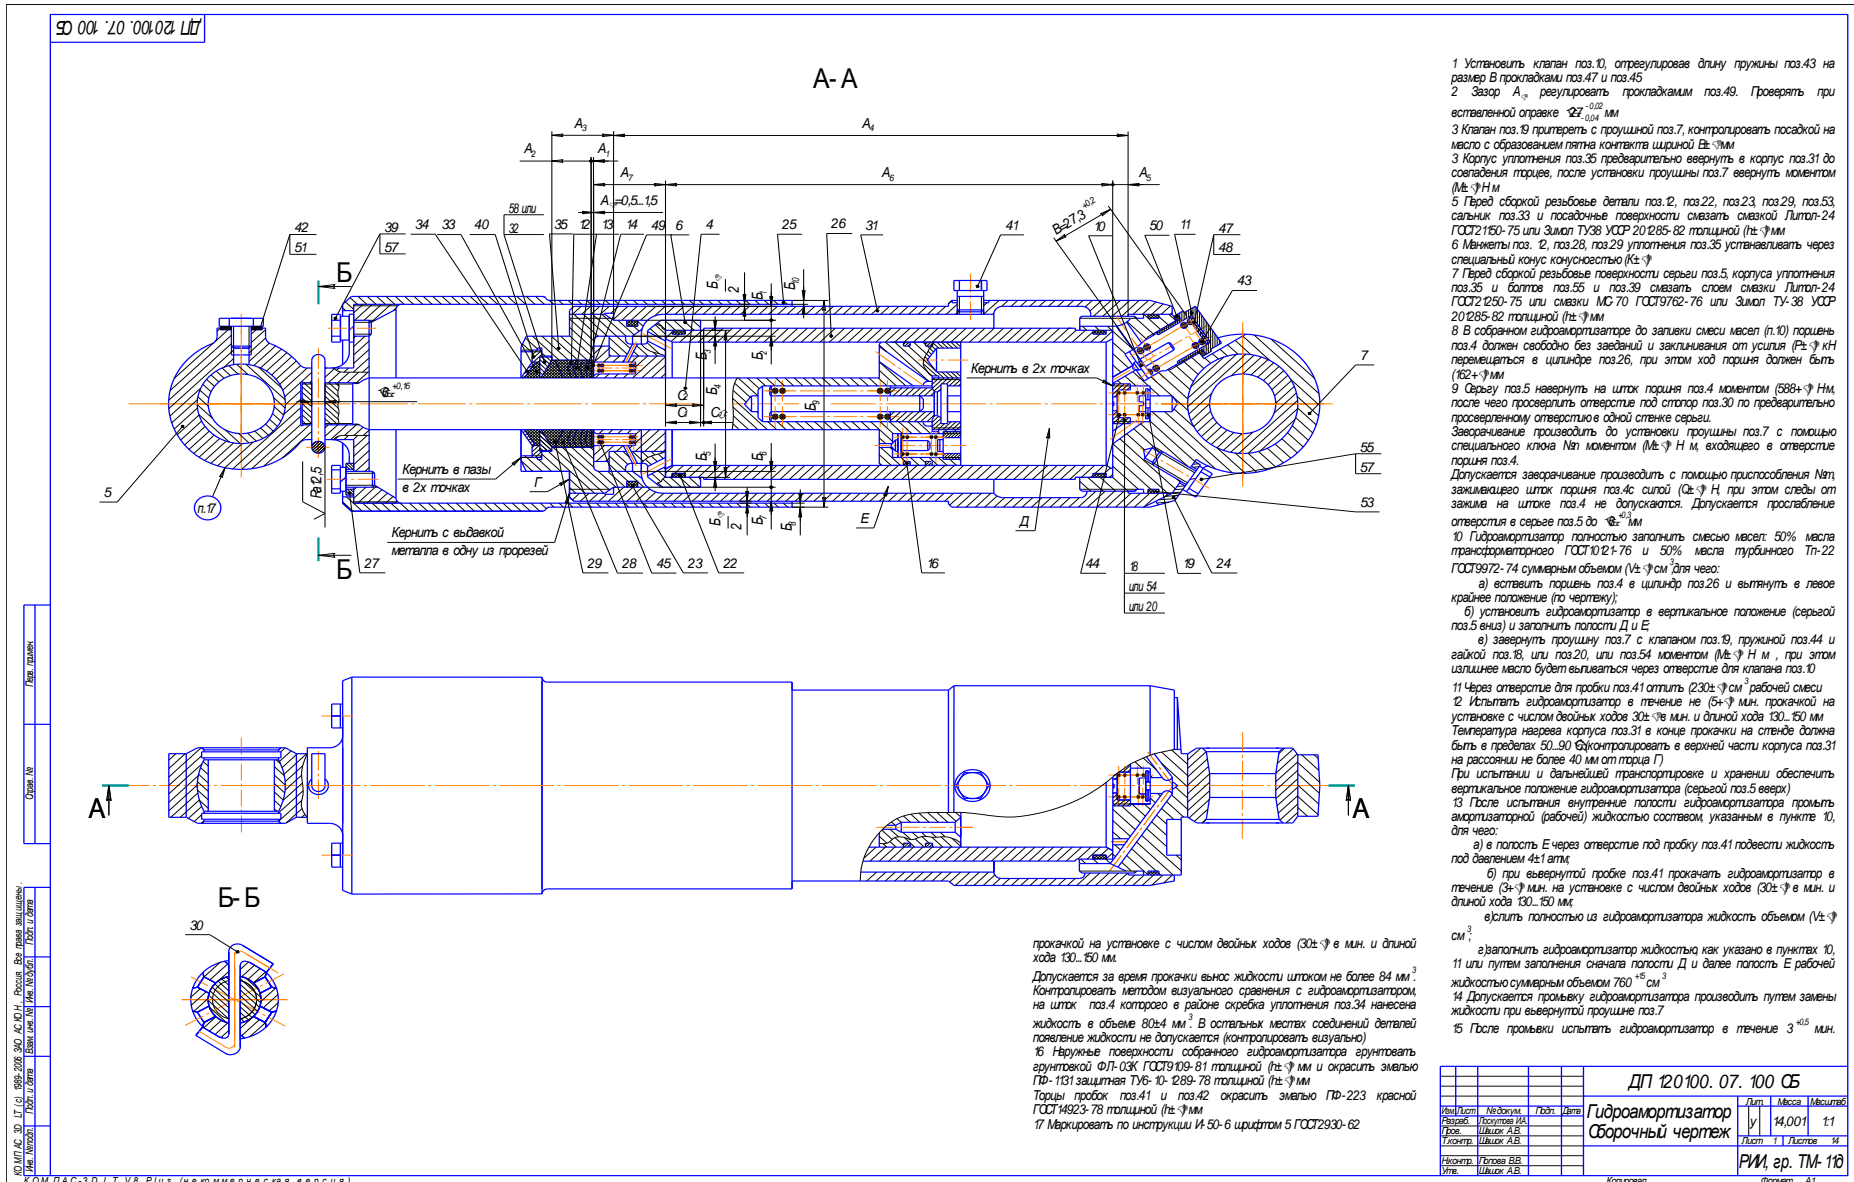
Гидроамортизатор. Сборочный чертёж
